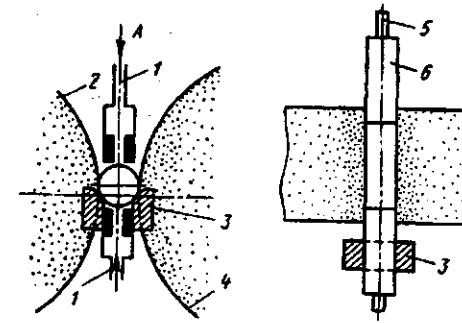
Схема бесцентрового шлифования поршневых пальцев с применением приборов активного контроля: 1 – сопла; 2 – шлифовальный круг; 3 – направляющая призма; 4 – ведущий круг; 5 – опорный нож; 6 – обрабатываемые детали
